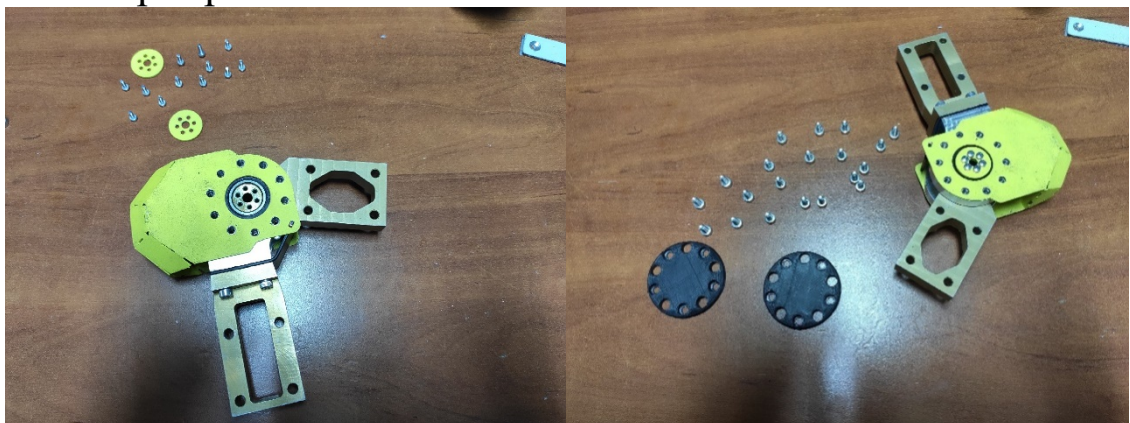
Место крепления шайб-фланцев и пластиковых накладок
